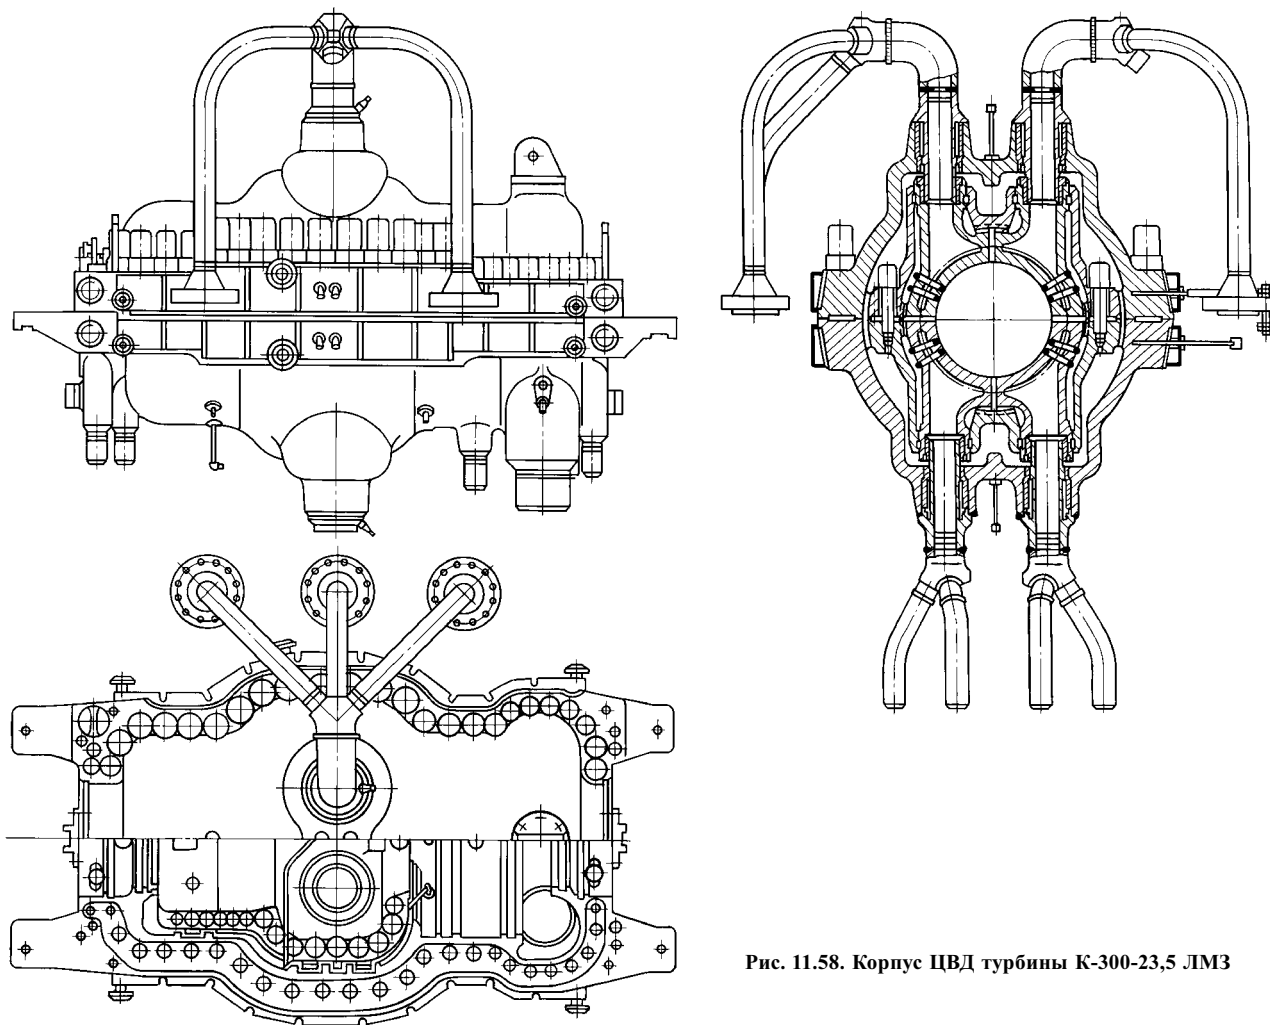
Корпус ЦВД турбины К-300-23,5 ЛМЗ
